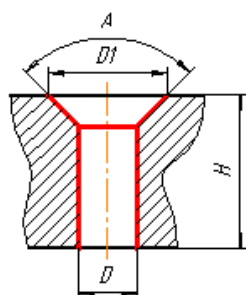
КТЭ цилиндрическое сквозное отверстие под крепежные детали с потайной головкой для поверхностей №17, 31, 36
